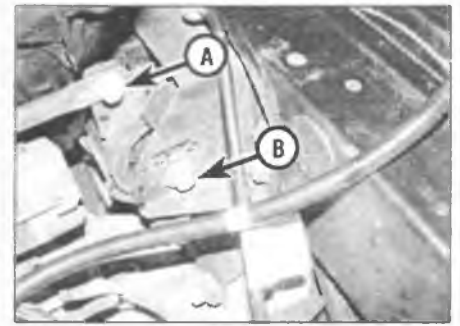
Отсоедините опорную штангу (А) и выверните анкерный болт опоры двигателя (В)
